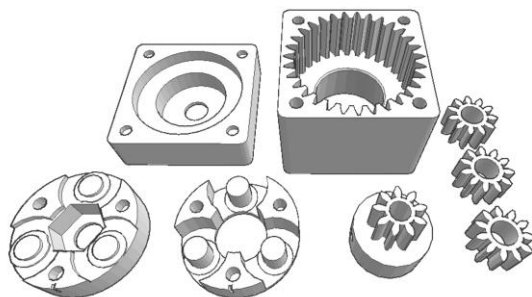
Редуктор планетарного механізму для крокового електричного привода
